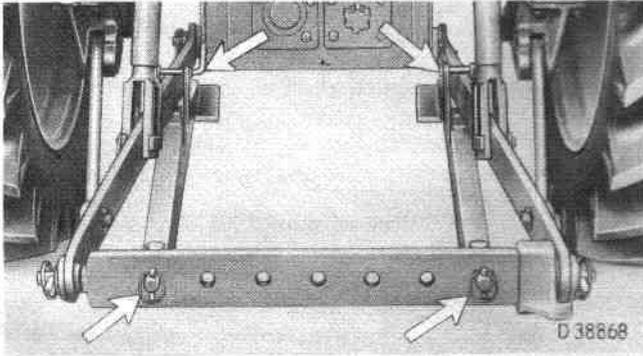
Fixation du dispositif auto cric à l'arrière
